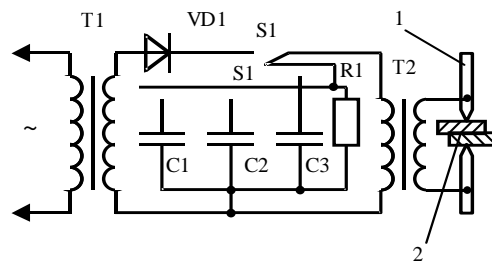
Схема конденсаторной сварки:
